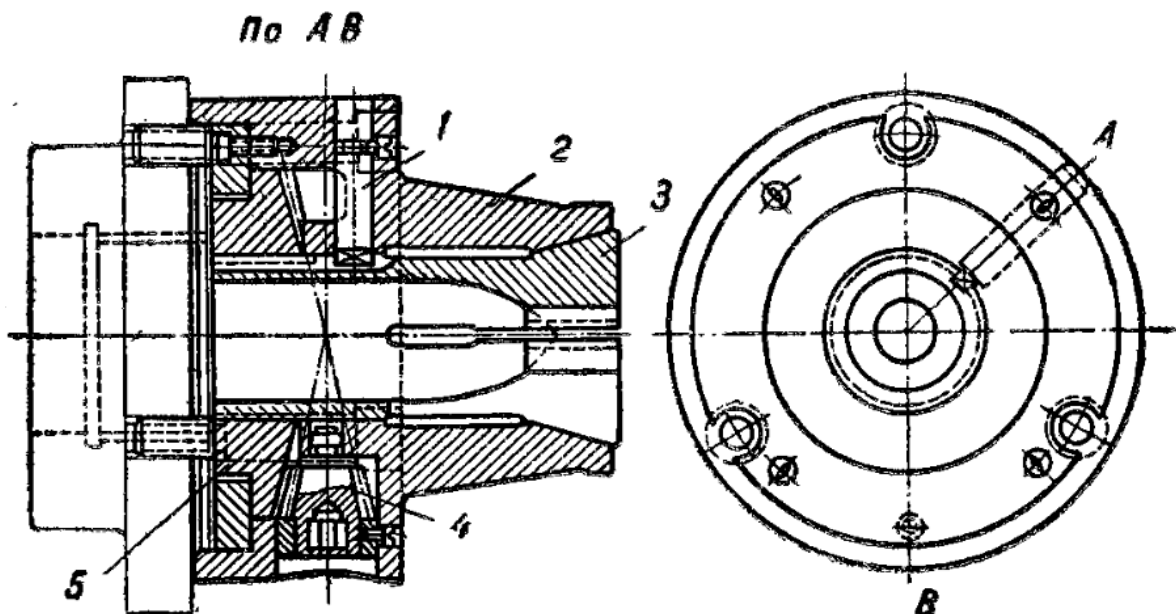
Універсальний цанговий патрон із затяжкою від ключа
